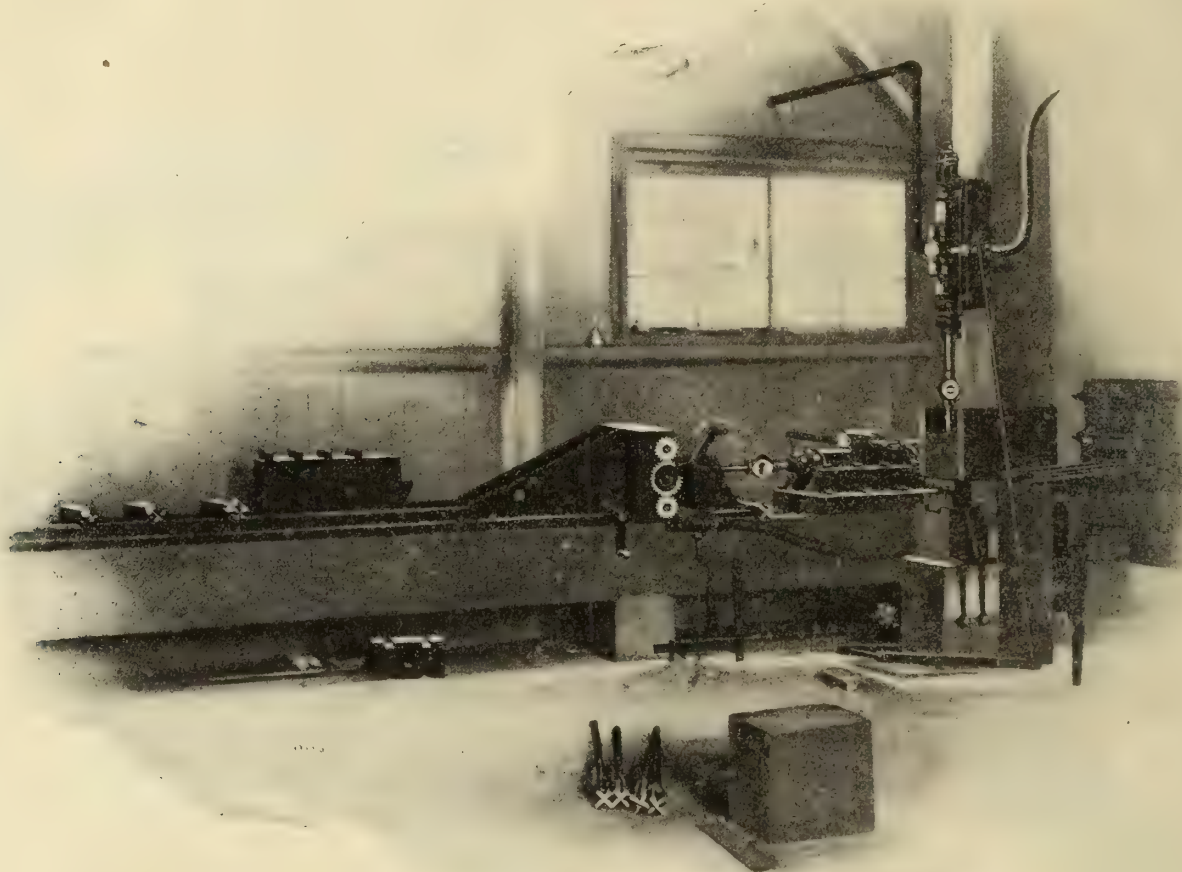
Schmiedemaschine für Bohrmeißel. Ingersoll-Rand Drill Co., New York-Berlin.
